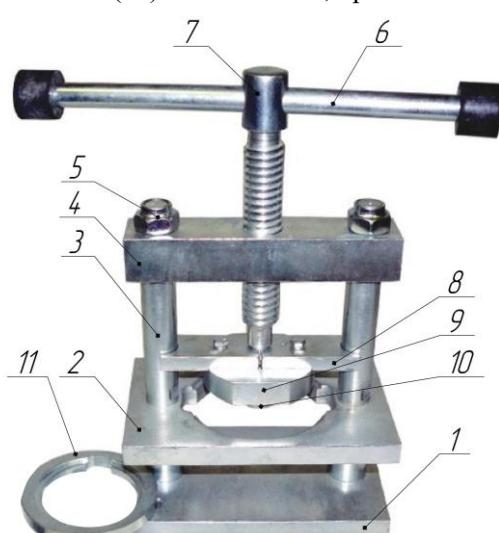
Пресс зуботехнический для выпрессовки гипса:
